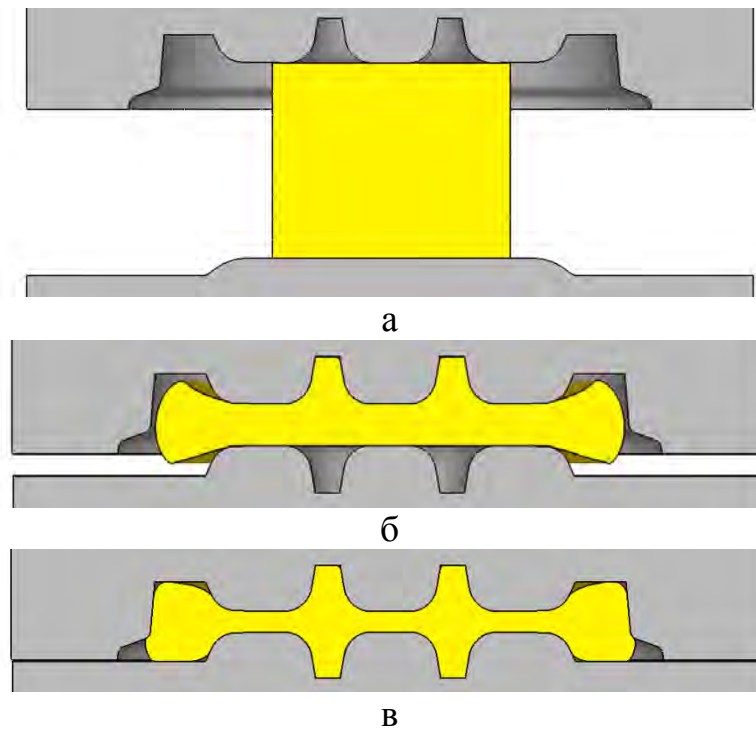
Формоизменение металла при штамповке из исходной заготовки Ø457 мм: а – начальный момент черновой штамповки; б - начальный момент чистовой штамповки; в – конечный момент чистовой штамповки
